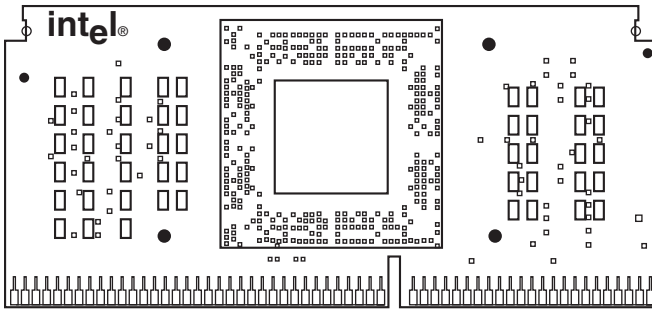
SEP-Gehäuse des Celeron-Prozessors in der Frontansicht
